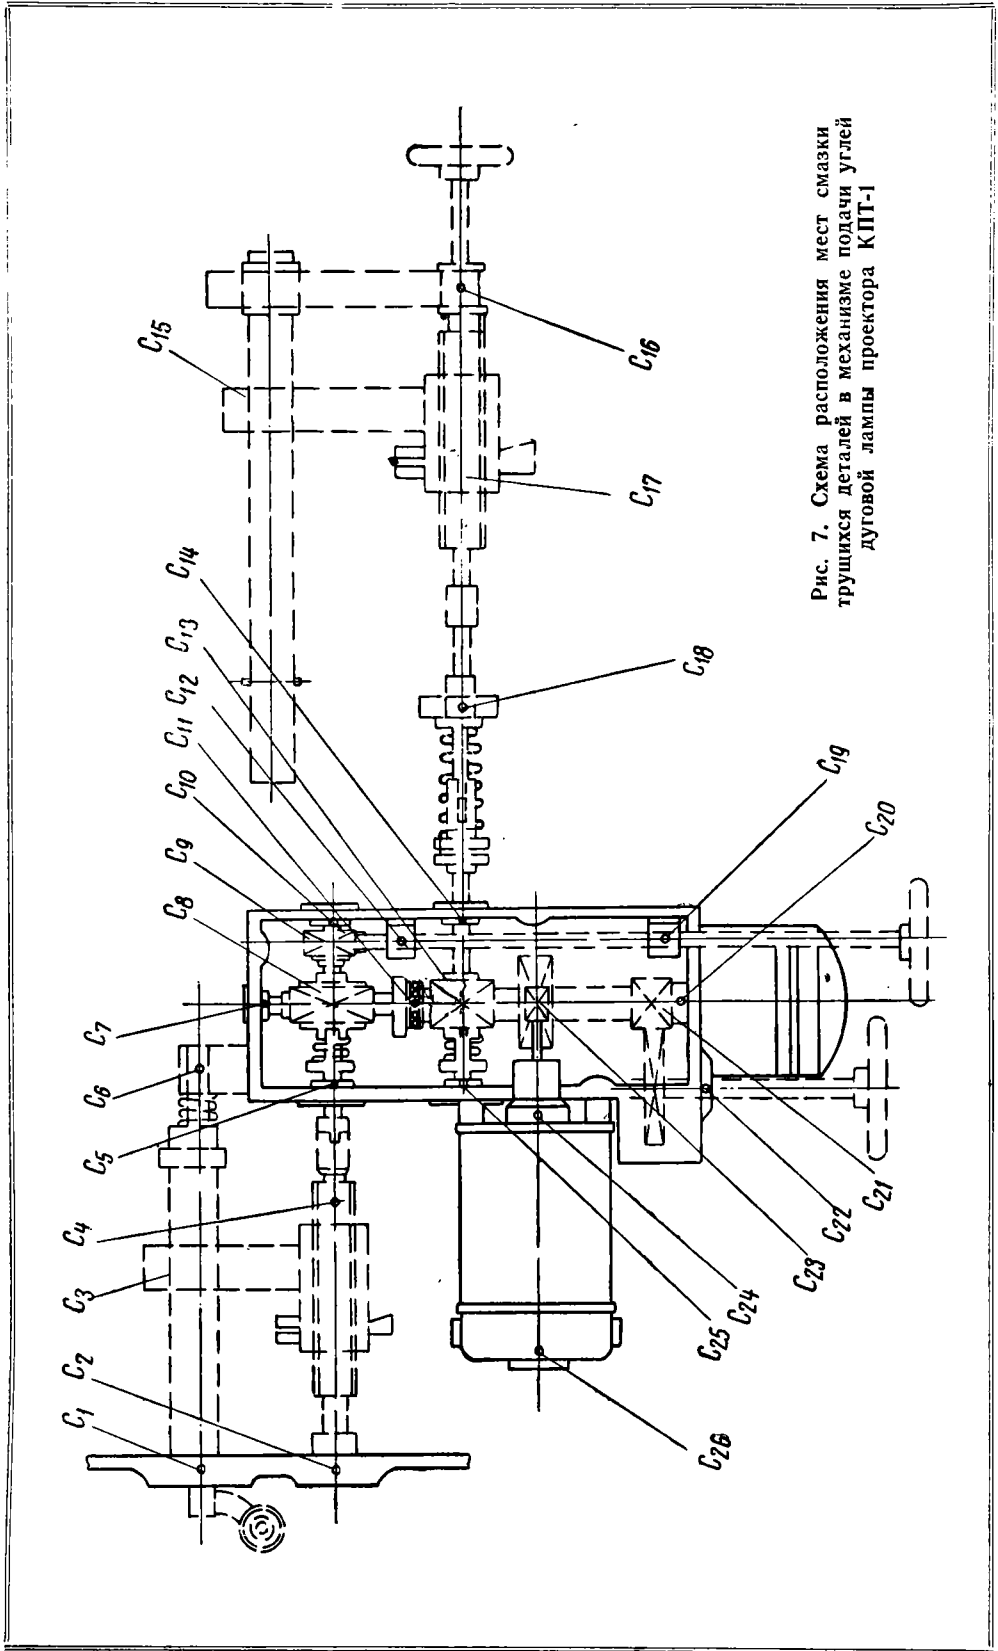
Схема расположения мест смазки трущихся деталей в механизме подачи углей дуговой лампы проектора КПП-1
